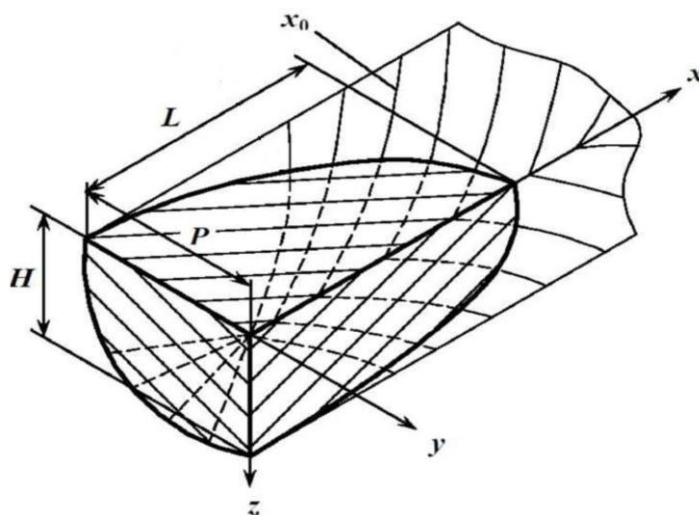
Образование кристаллитов в сварочной ванне эллипсоидного вида
